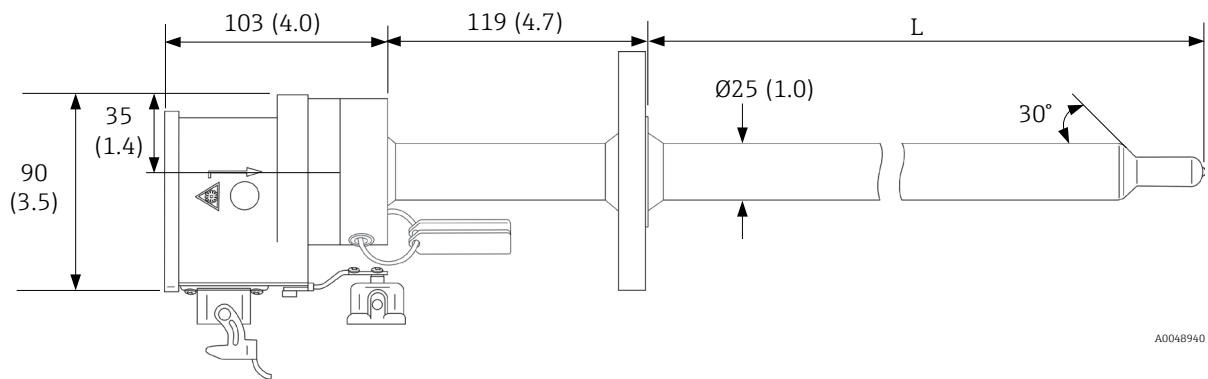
Sonde Rxn-41 1". Dimensions : mm (in)
